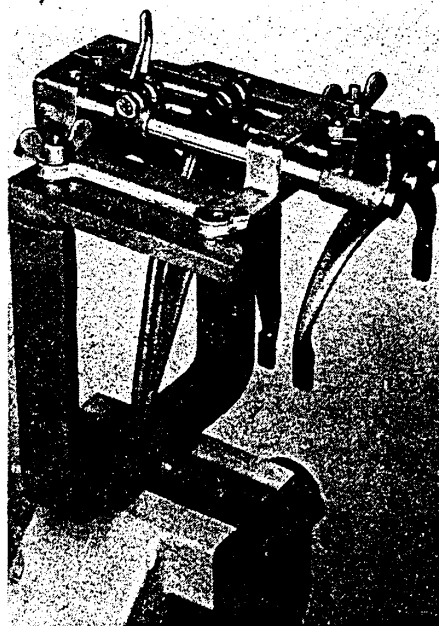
Schaltbrücke auf De- und Montagevorrichtung befestigt
